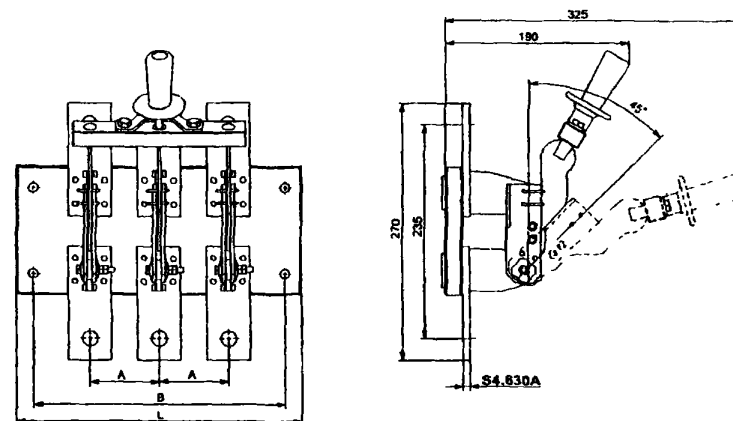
Разъединитель РЕ19 трехполюсный с центральной штангой, переднего присоединения шин
